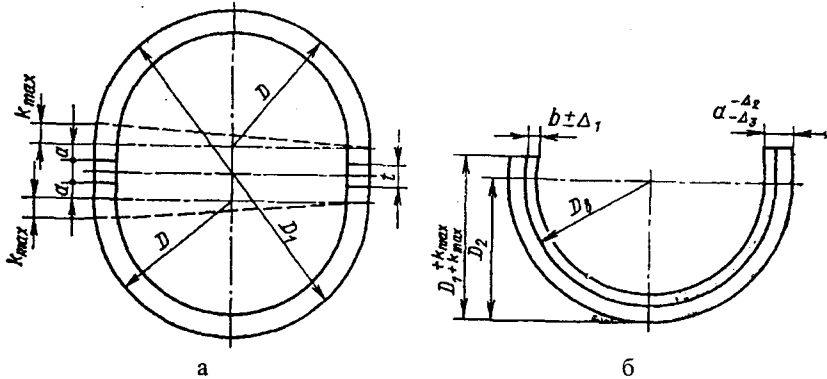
Розрахункові схеми: а – для визначення діаметру заготовки перед розрізанням; б – для визначення внутрішнього діаметру вкладиша перед заливкою бабітом.
